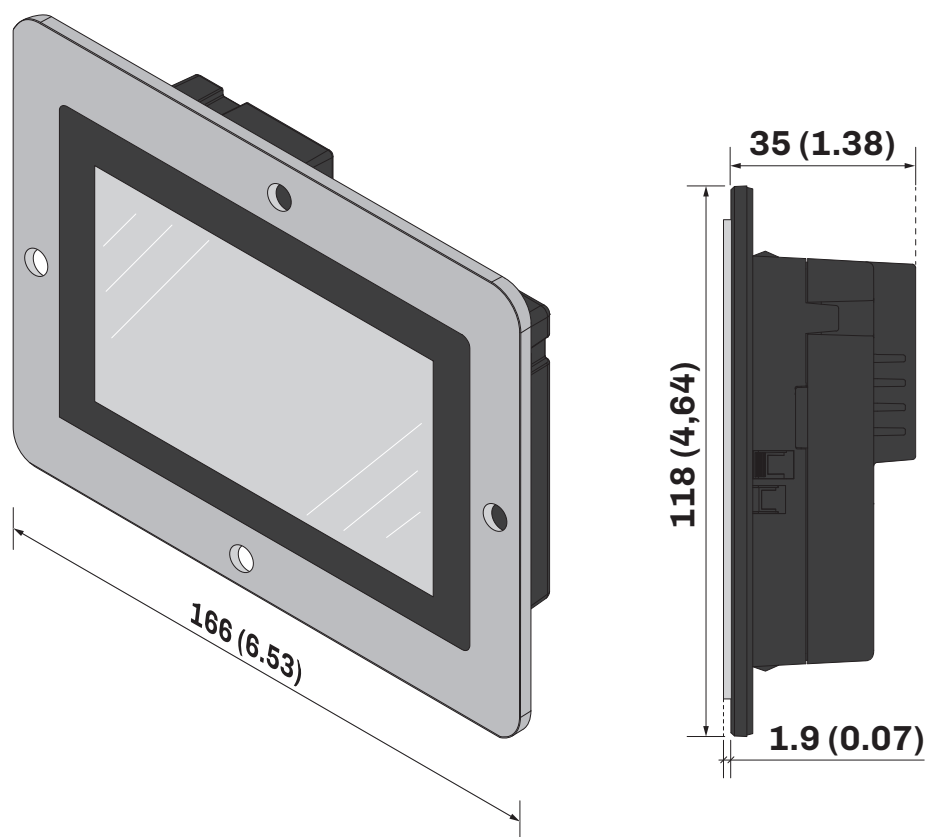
Dimensioni interfaccia utente Vcolor 739 M a montaggio a filo
